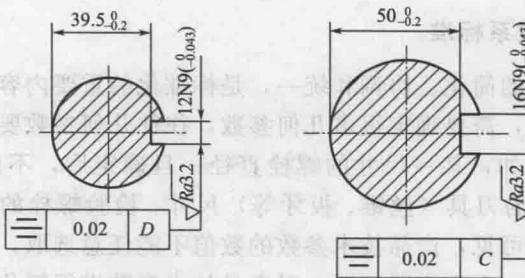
减速器输出轴的尺寸、形位、表面粗糙度的公差要求
